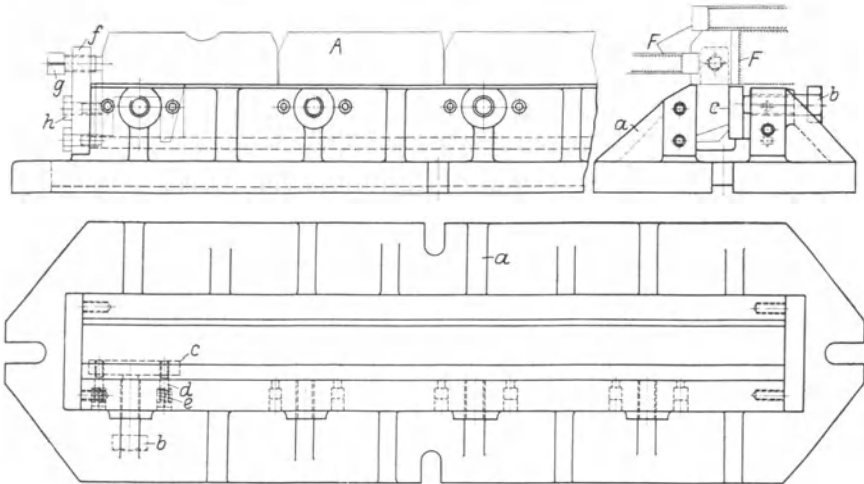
Fräsvorrichtung zum Fräsen mehrerer Flächen.
